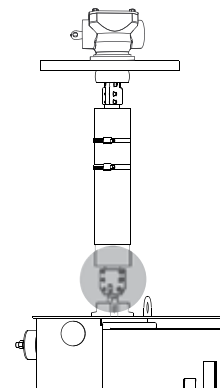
Соедините вал квадратного сечения с механизмом моторного привода
